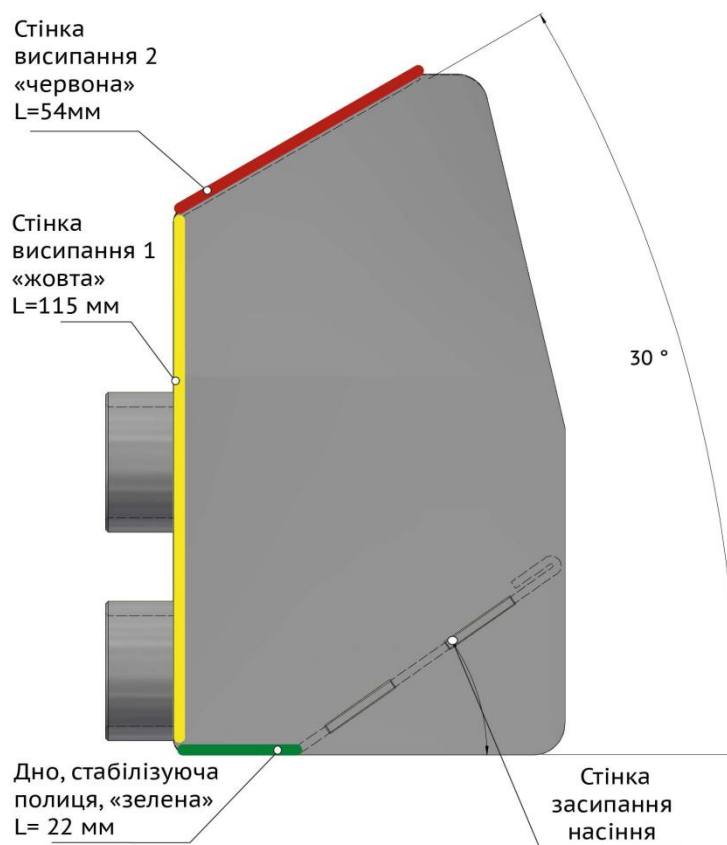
Геометрична схема робочих поверхонь модернізованого ковша 30°
